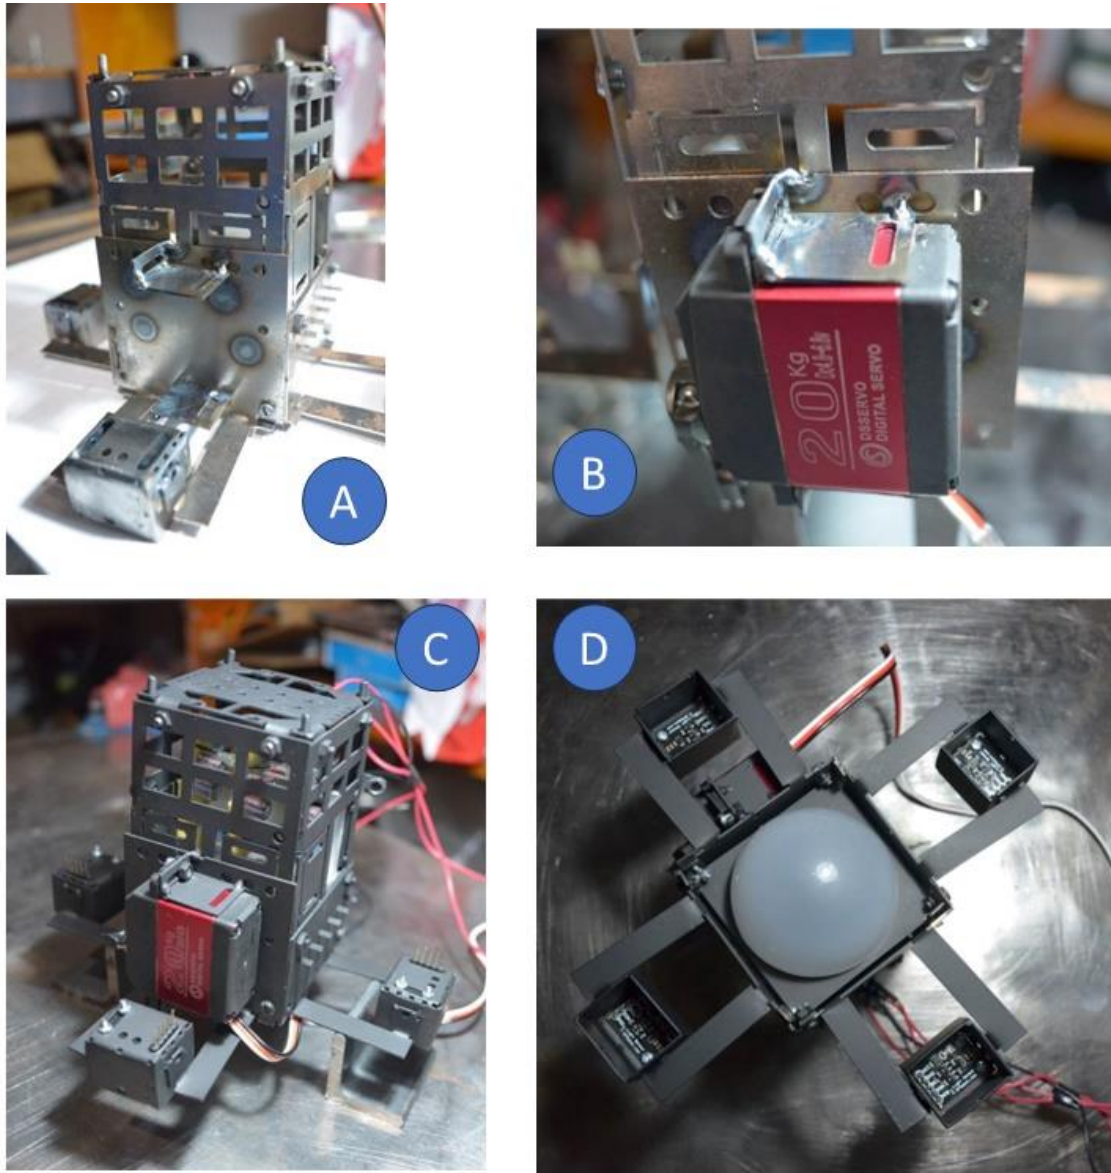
Fabricación Cabezal de iluminación. (A) Cabezal de iluminación muestra marcas de calor localizado donde se realizó soldadura TIG, (B) Detalle del soporte para el motor servo para las persianas, (C) Vista general superior del Cabezal completamente ensamblado y poblado de electrónicos, (D) Vista general inferior del Cabezal, al centro el difusor de luz y a las orillas los sensores de luz.
